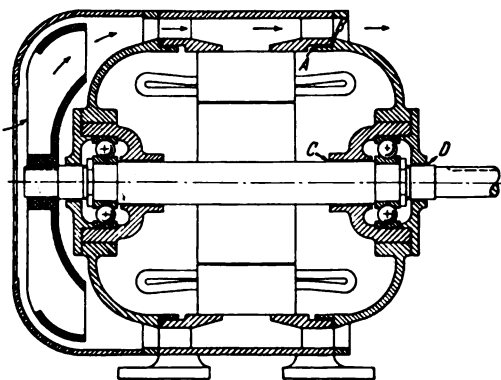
Mantelgekühlter, explosions sicherer Motor.
